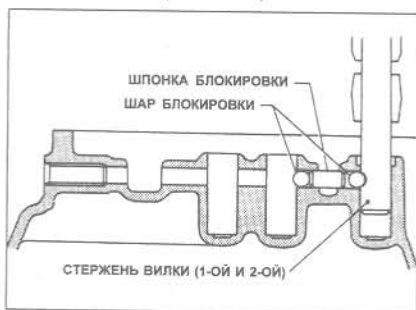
Шары блокировки и плунжер стержня вилки смещения 1/2 передач (Глава 14)
